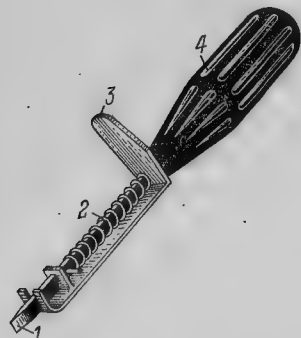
1 — лезвие (стержень); 2 — пружина; 3 — лапка; 4 — ручка
